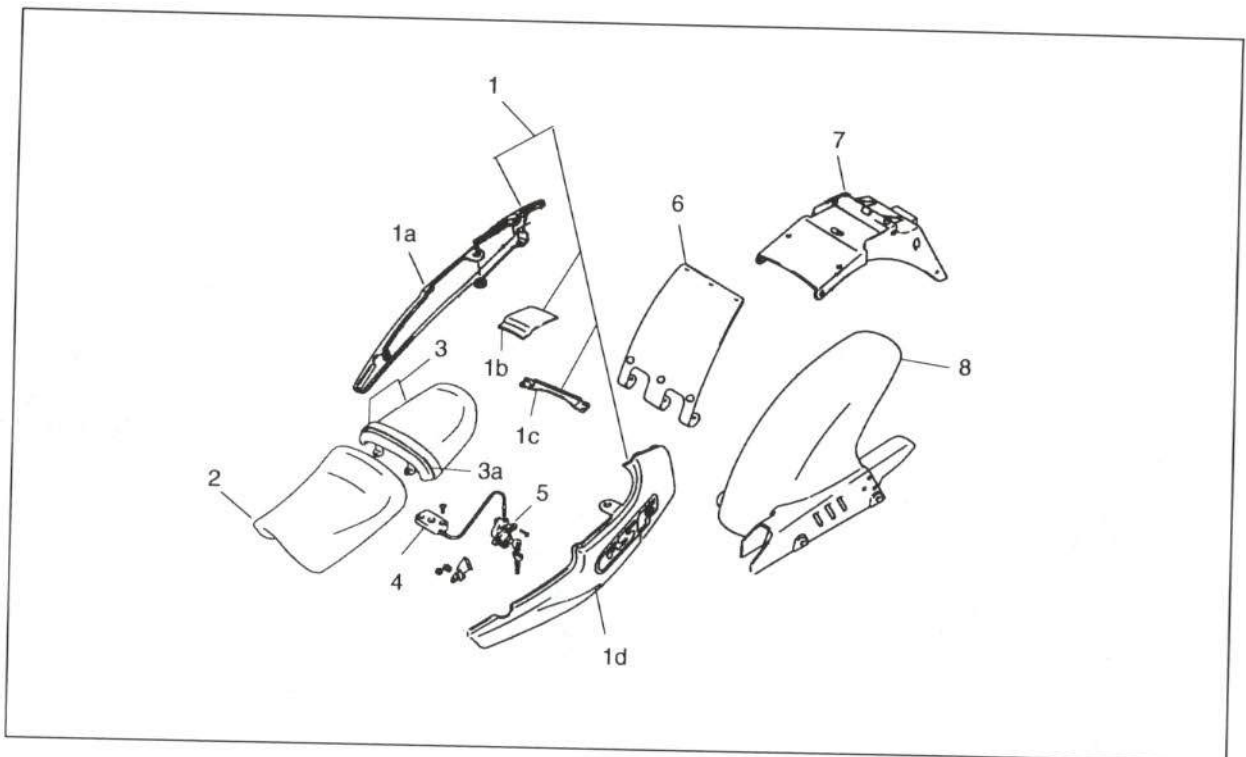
Despiece de las piezas exteriores de la parte trasera
